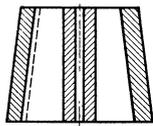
Geteilte Schnittplatte, auf Amboßplatte zu stellen.
